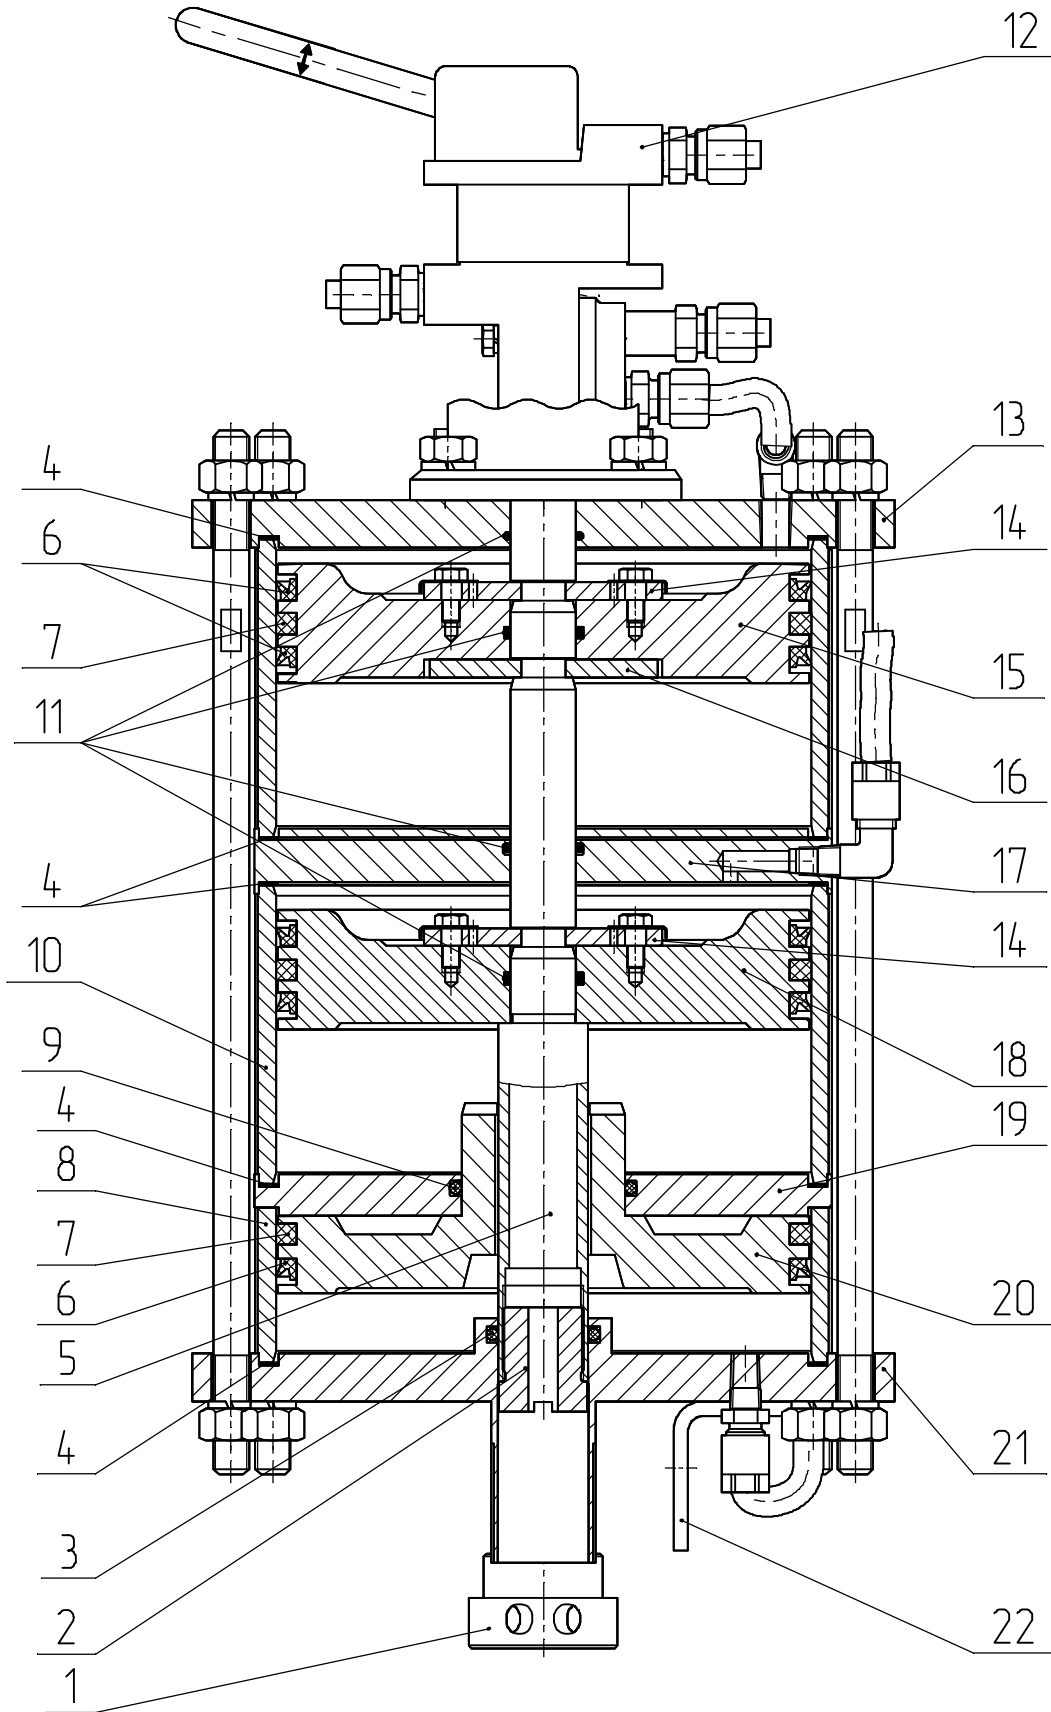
Конструкция трехпоршневого пневмоцилиндра
